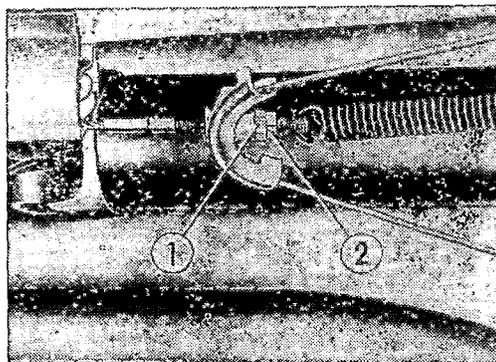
Натяжное устройство троса стояночного тормоза
